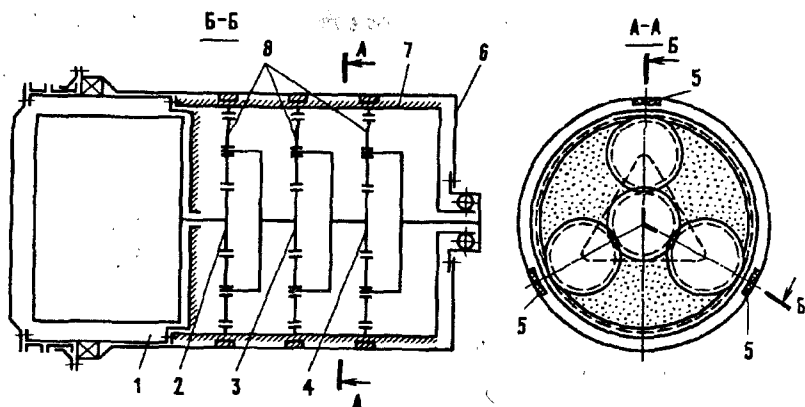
Схема планетарного редуктора с магнитопорошковой смазкой: 1 — электродвигатель; 2, 3, 4 — центральные шестерни; 6 — магнит; 7 — эпитцкл; 8 — сателлиты
